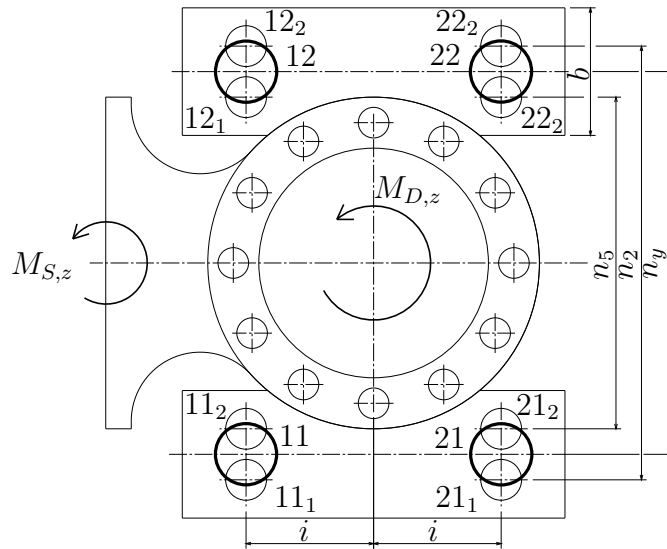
Annahme für die Berechnung der acht Befestigungsschrauben
